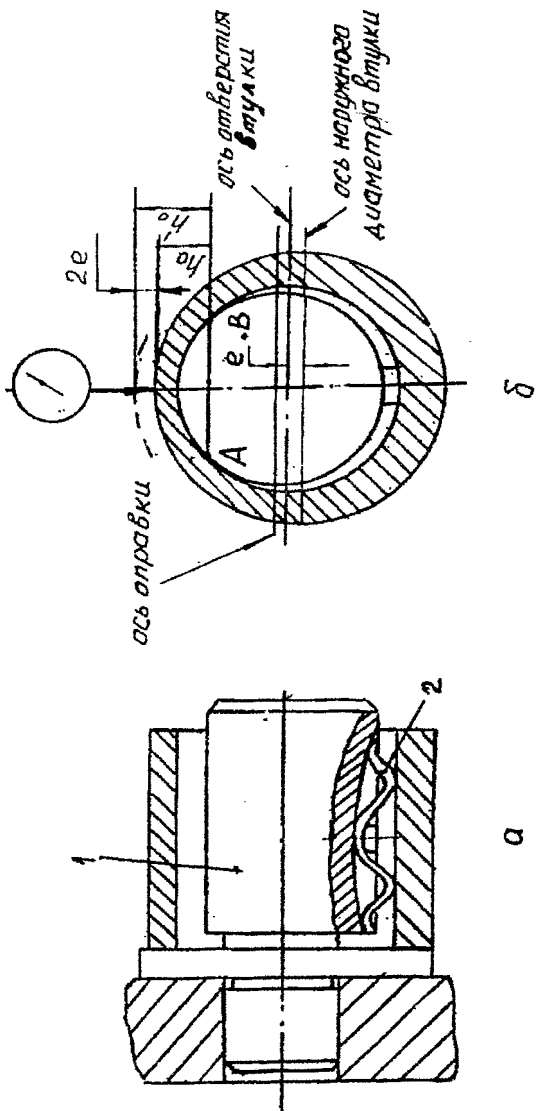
Конструкция гладкой оправки со срезанной площадкой (а) и схема контроля детали (б)
